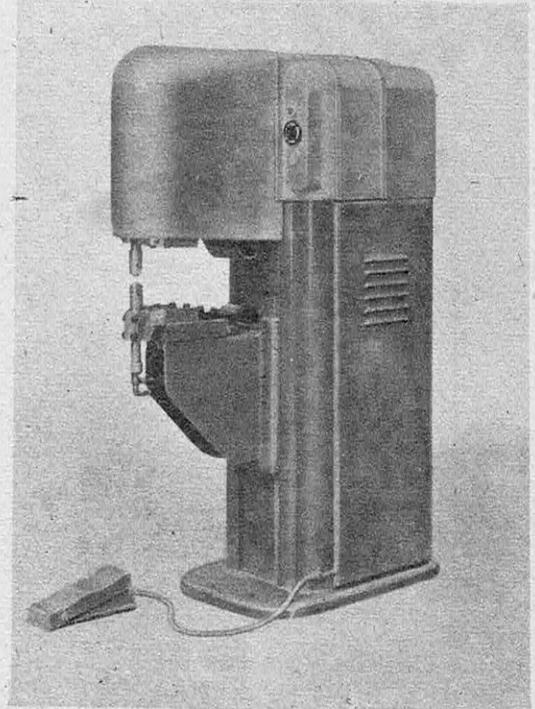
MACHINE A SOUDER PAR POINTS (LA SOUDURE ÉLECTRIQUE)
